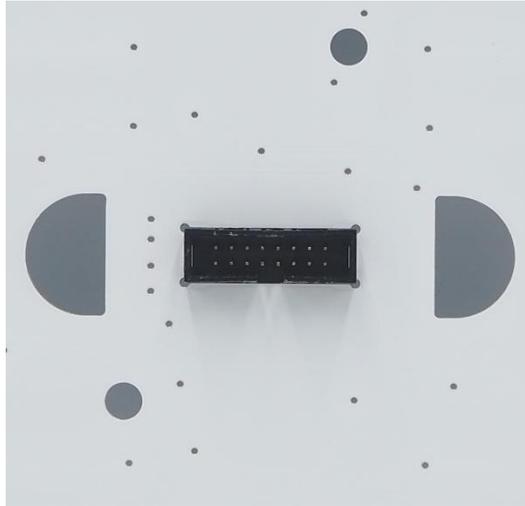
PCB píxel blanco detalle conector y agarres vista trasera.
